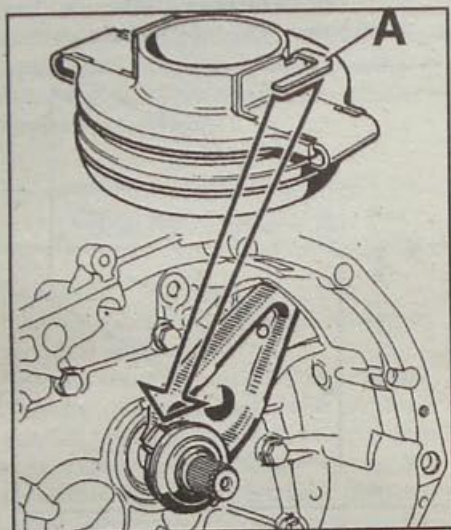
Установка подшипника выключения сцепления на направляющую втулку:
